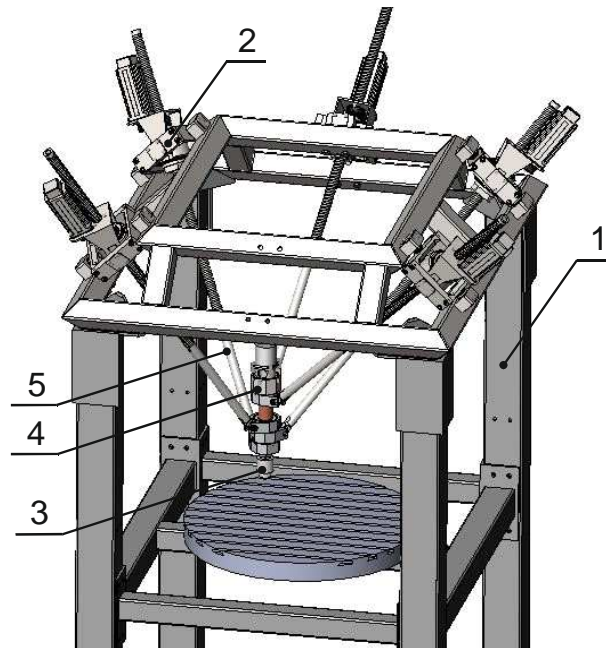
Модель дослідного зразка верстата з механізмом «пентапод»: 1 – основа; 2 – шарнірні опори; 3 – робочий орган; 4 – шарнірні опори; 5 – штанги
